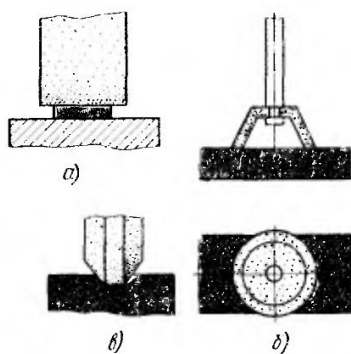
Шлифование заготовок плоскошлифовальных станках
